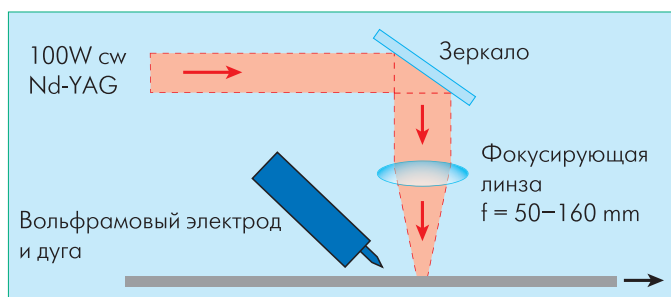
Схема экспериментальной установки для исследования гибридной (TIG-лазер) сварки в режиме плавления
